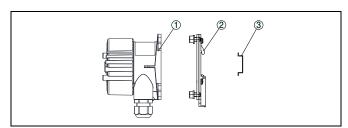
$VEGADIS\,81\,y\,82\,c$  on carcasa de aluminio y acero inoxidable para el montaje en regleta de montaje
